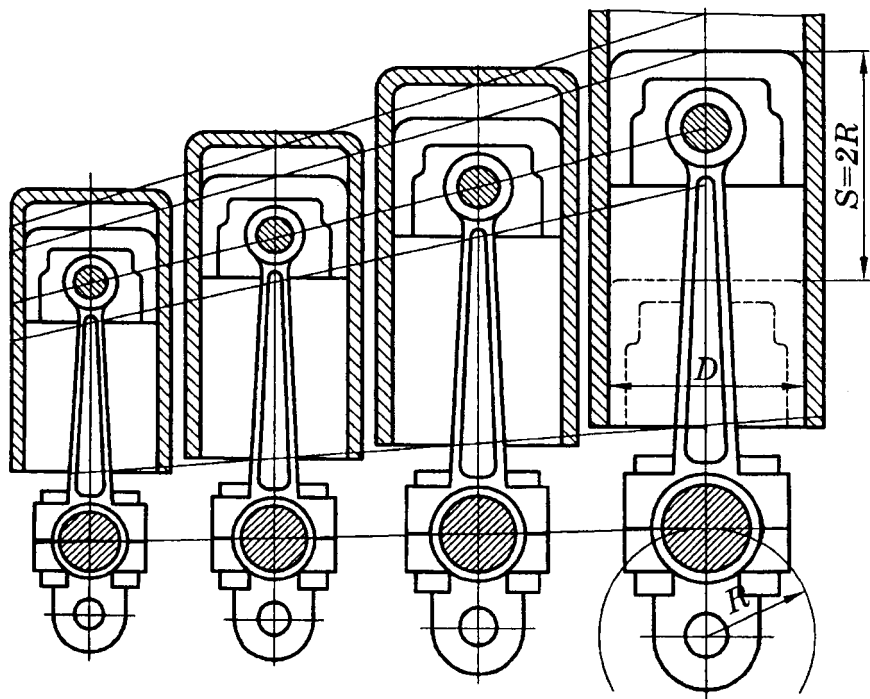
Размерно-подобный ряд поршневых двигателей
